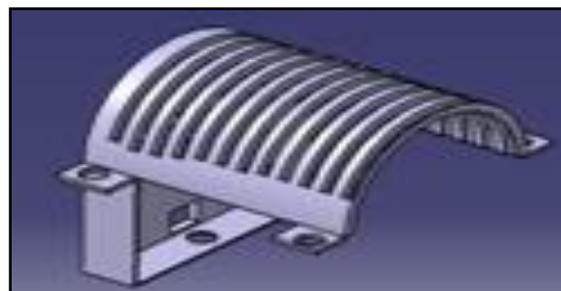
l'outil de protection et de fixation de l'outil de sertissage
